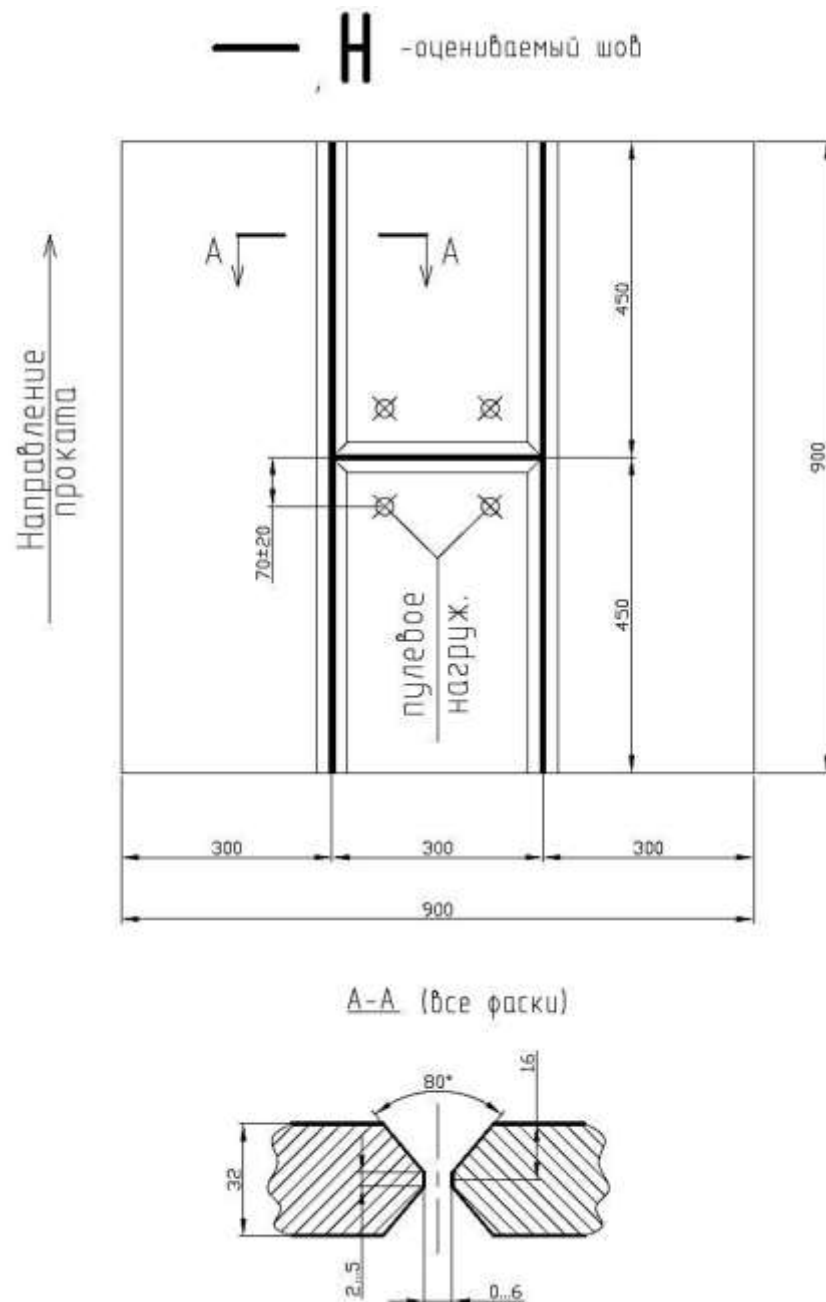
Сварная проба для стрельбовых испытаний
